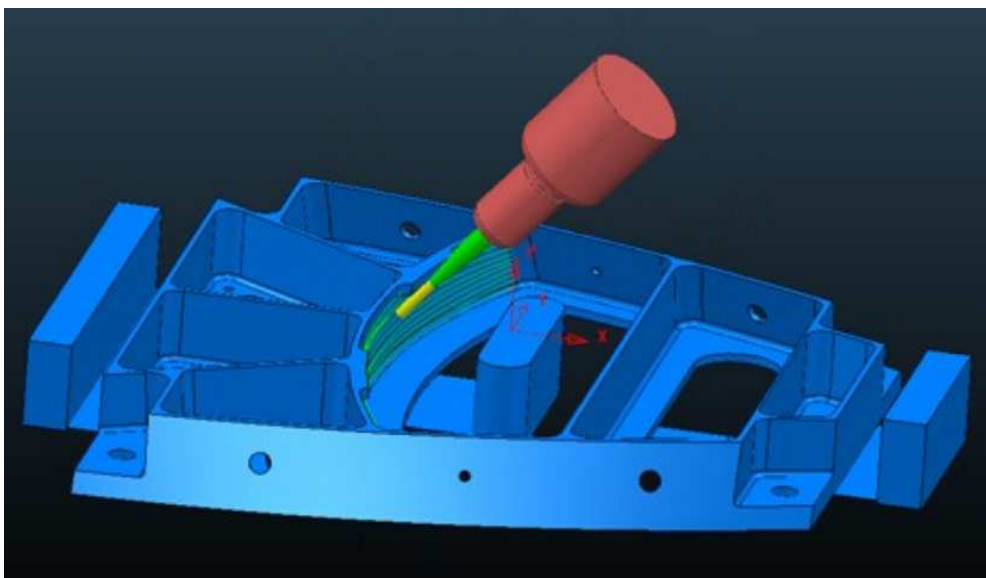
5-osé frézování v programu PowerMILL [10]
